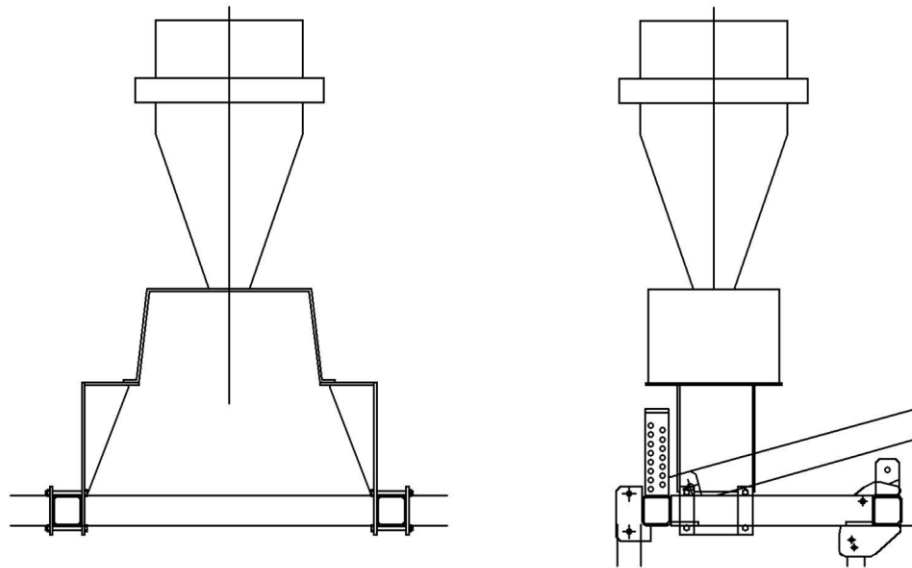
Montage der Sämaschine SP 5 auf dem KUS-Rahmen.
